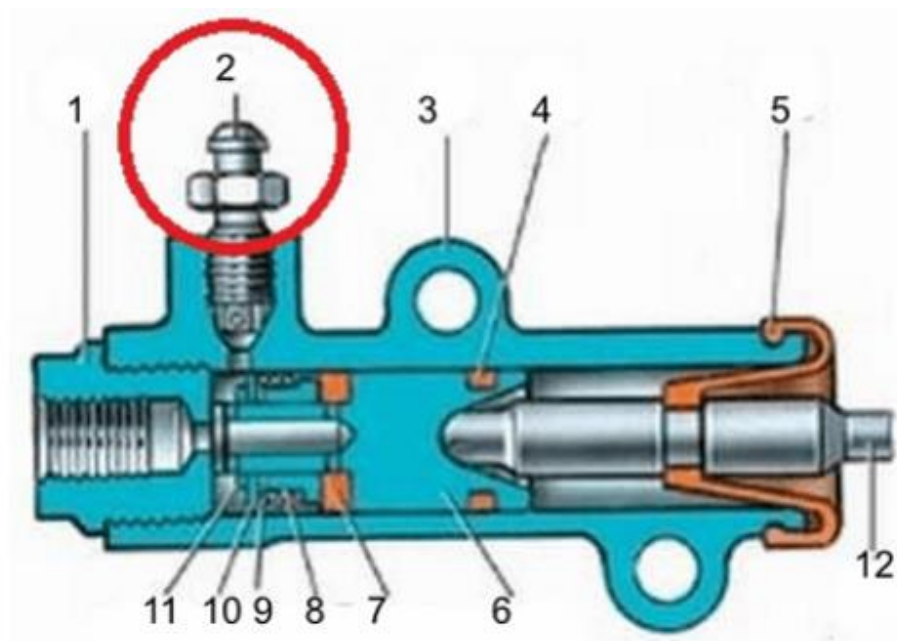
Рабочий цилиндр привода сцепления ВАЗ 2107:
